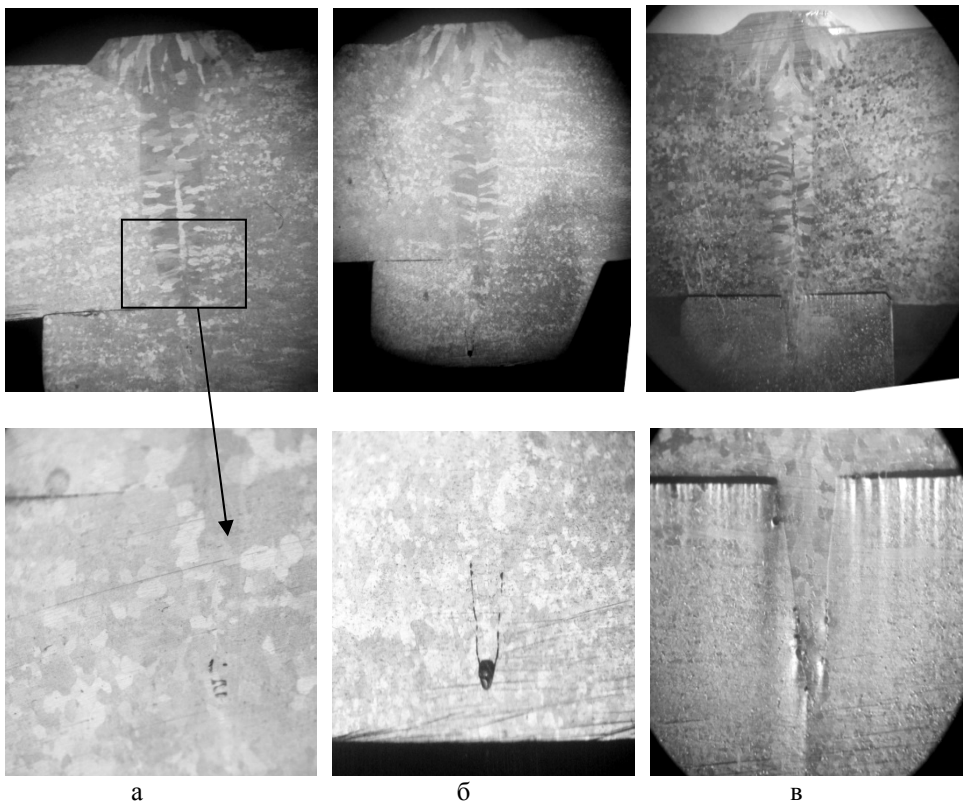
Макроструктура зварного з'єднання деталей з титанового сплаву ВТ22 з дефектами в корені шва:
